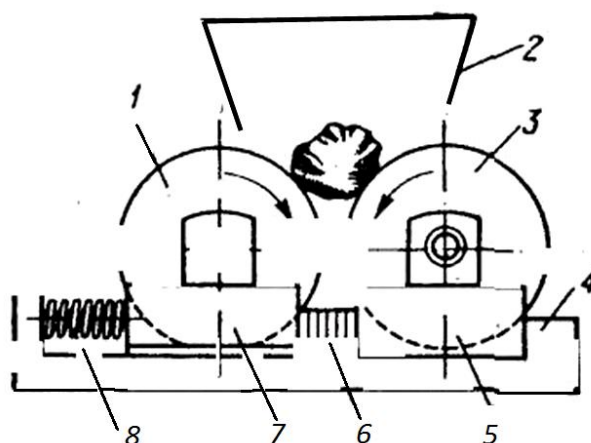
Схема действия двухвалковой дробилки: 1, 3 – валки; 2 – загрузочная воронка; 4 – станина; 5, 7 – подшипники; 6 – прокладка; 8 – пружина
